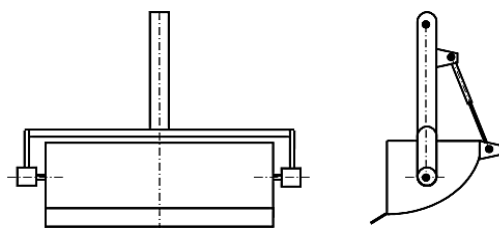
Схема поворотного ковша с виллообразной рукоятью
